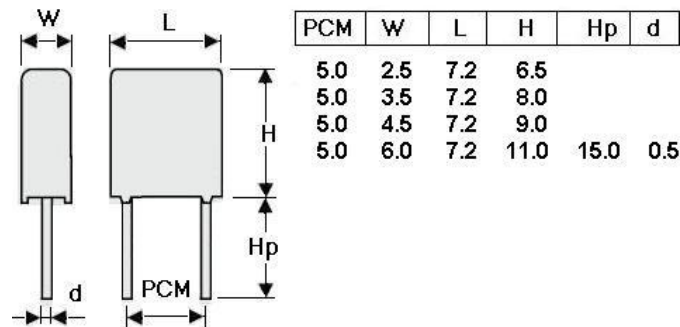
Габаритні розміри конденсатора В32529С1102J000
